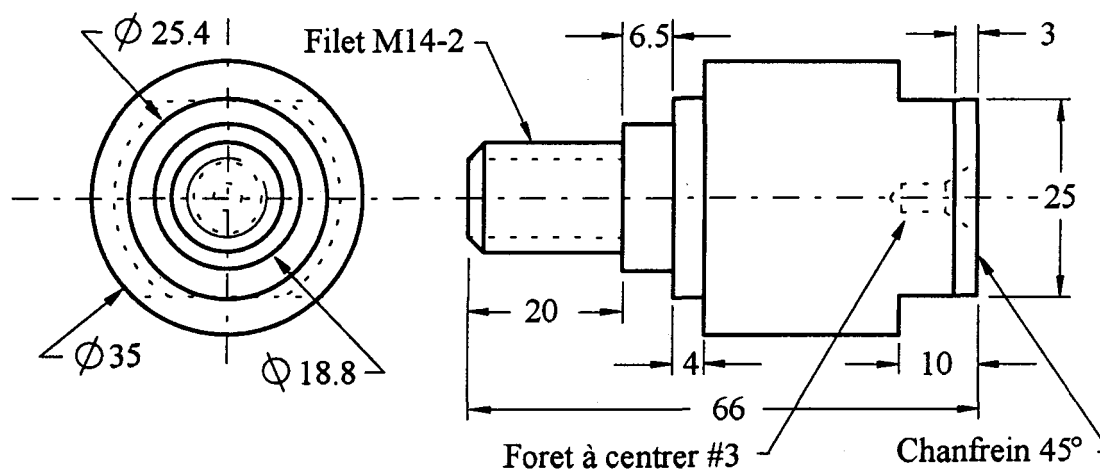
Assemblage du collecteur cylindrique (les dimensions sont exprimées en mm).
